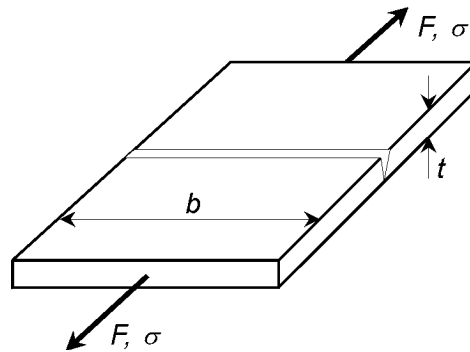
Soldadura a tope, tensiones normales
